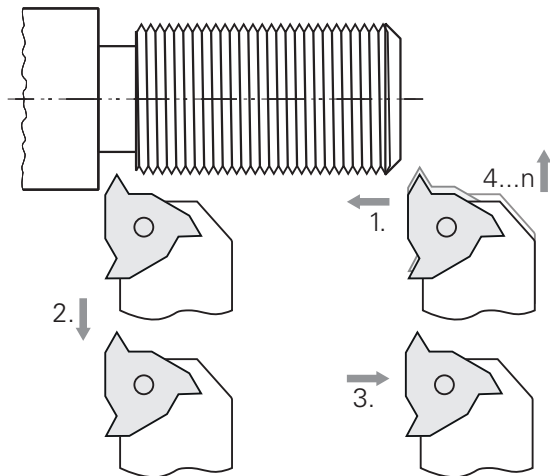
Beispielwerkstück – Gewinde fertigen
